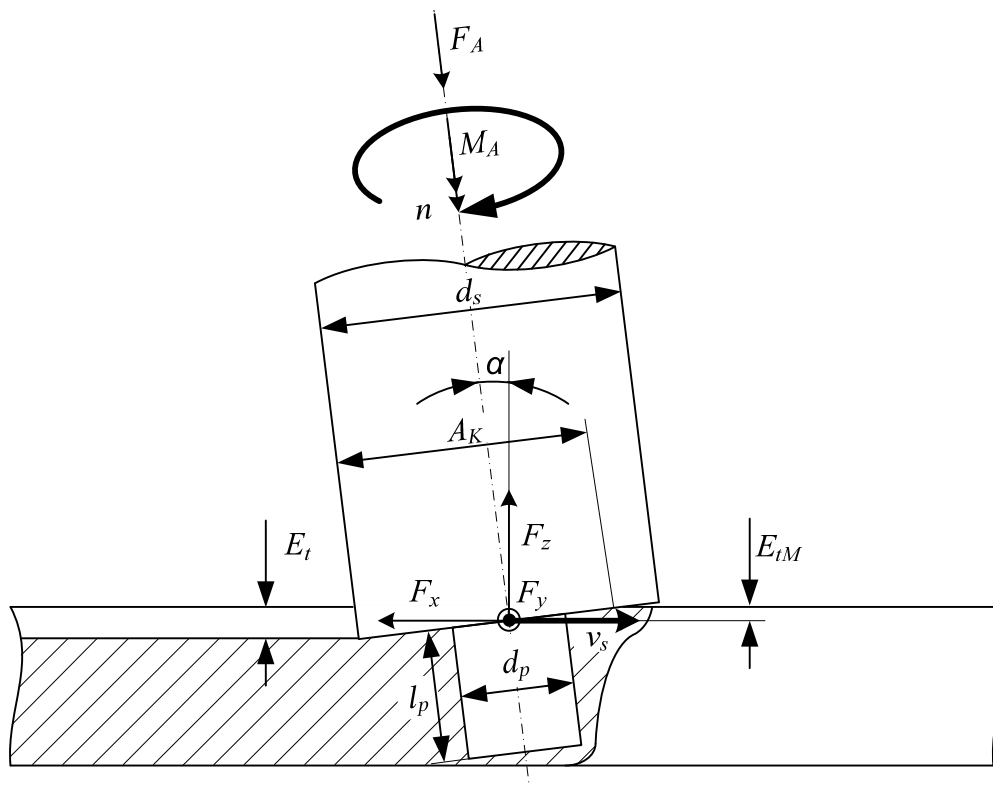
Prinzipskizze des FSW-Prozesses in einem Längsschnitt durch die Schweißnaht (schraffiert)
